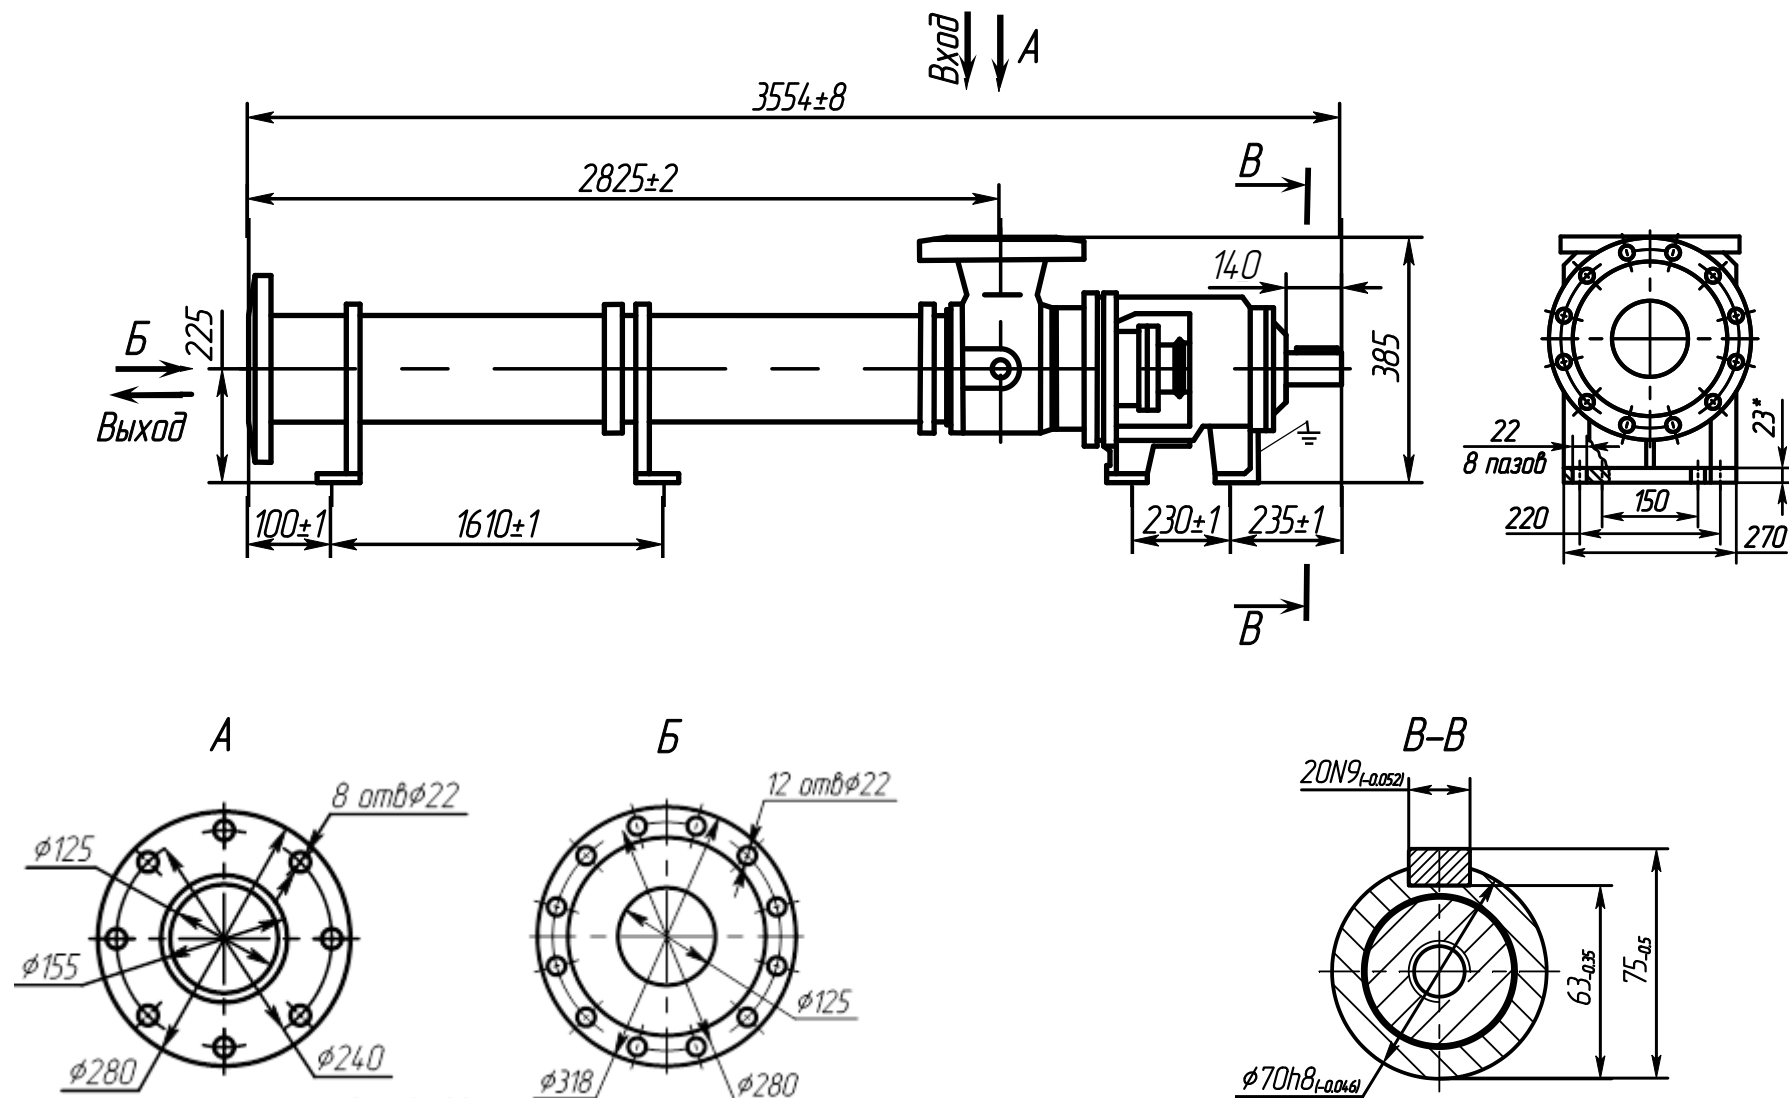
Габаритный чертёж насоса Н1В 120/25-15/16
